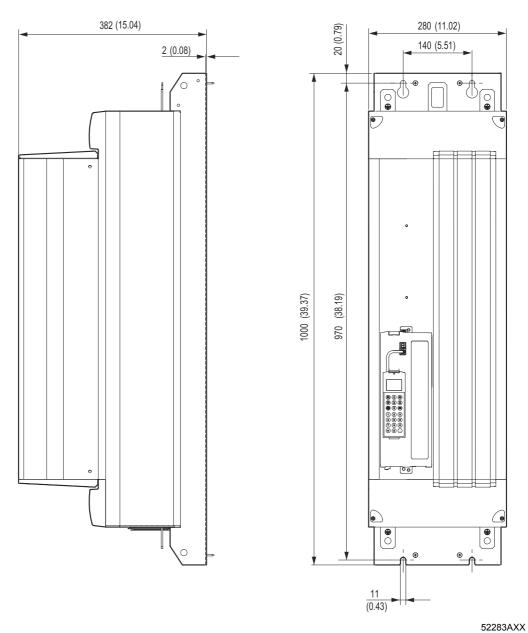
Dimensões MDX61B, tamanho 6, dimensões em mm (in)
